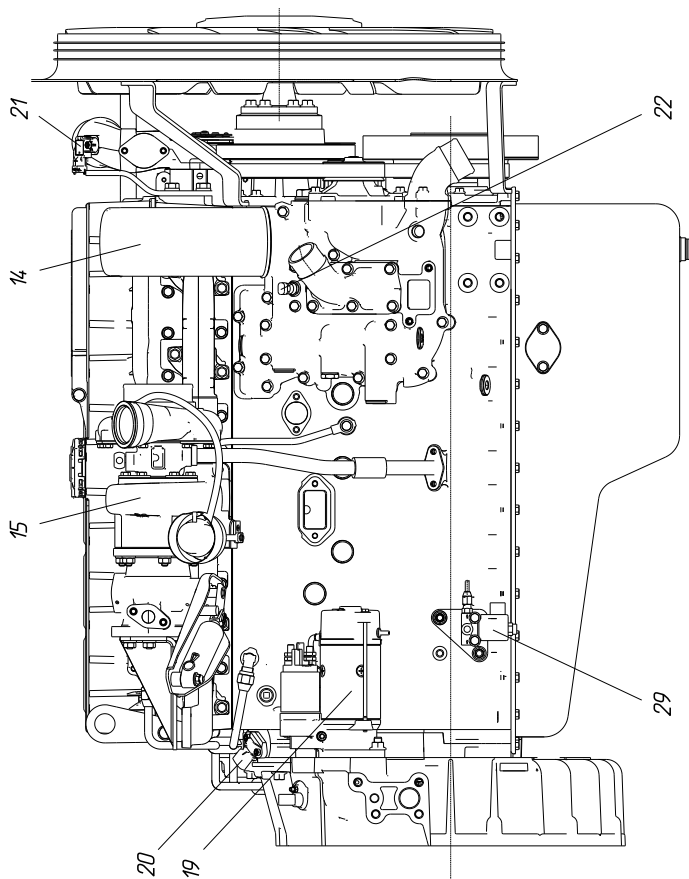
Расположение агрегатов и узлов двигателя ЯМЗ-Э5367 (вид справа):
